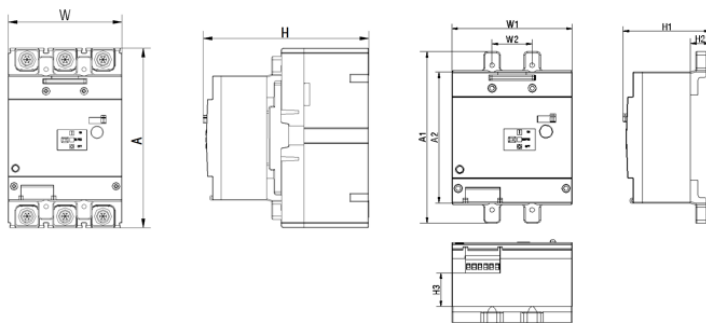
Габаритны и установочные размеры привода моторного МП-330
